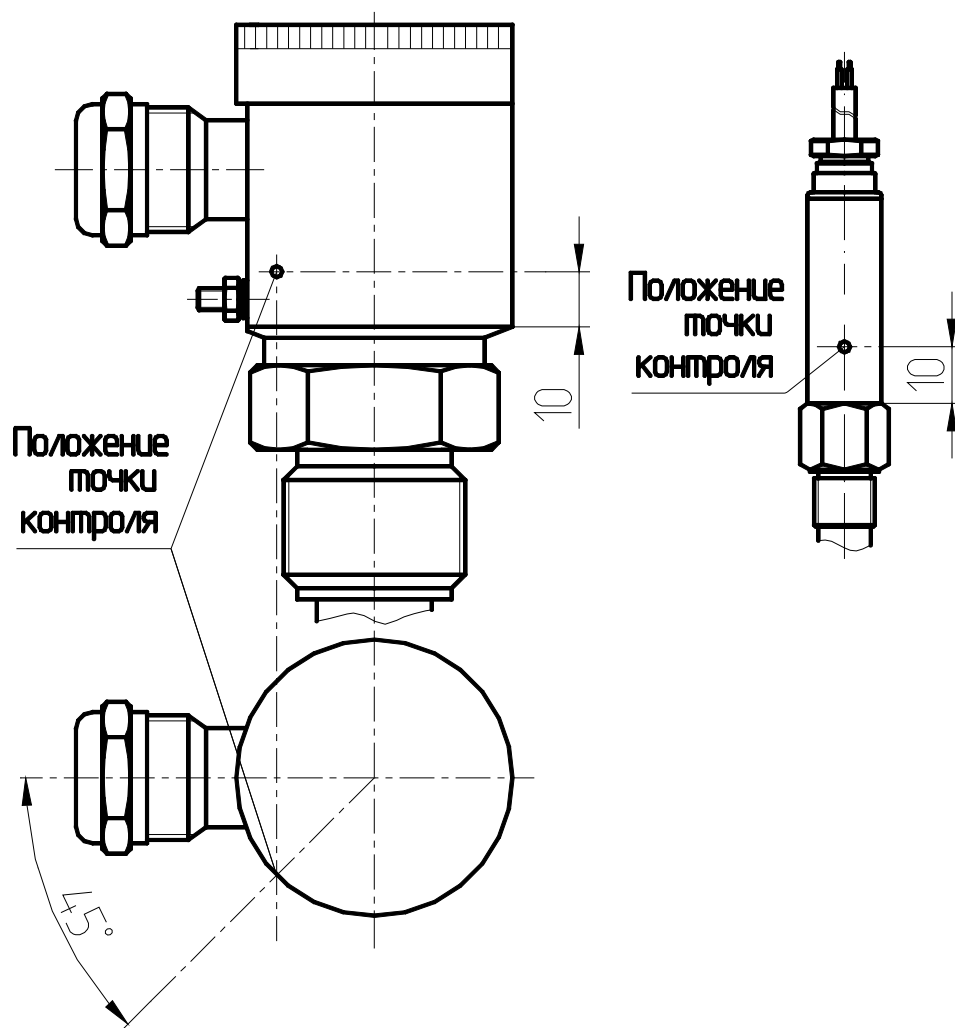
Положение точки для проверки магнитом на корпусах сигнализаторов UTS
